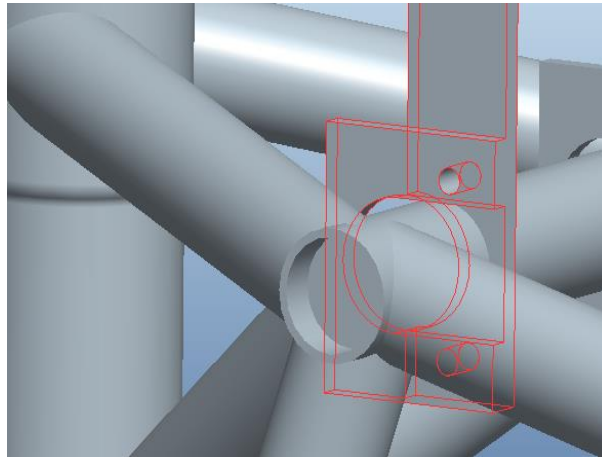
Pieza auxiliar del potro de soldadura con forma de media luna
